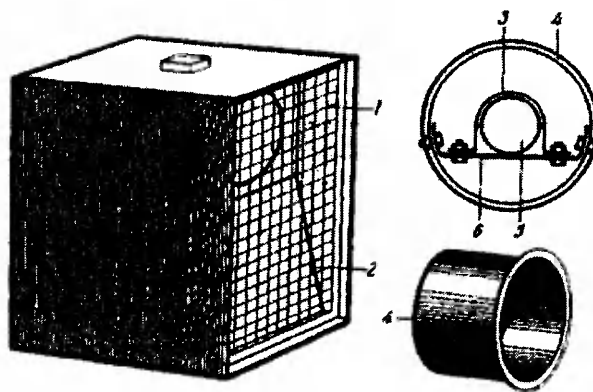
Несущий элемент двигателя вентилятора и крепящий хомут.
